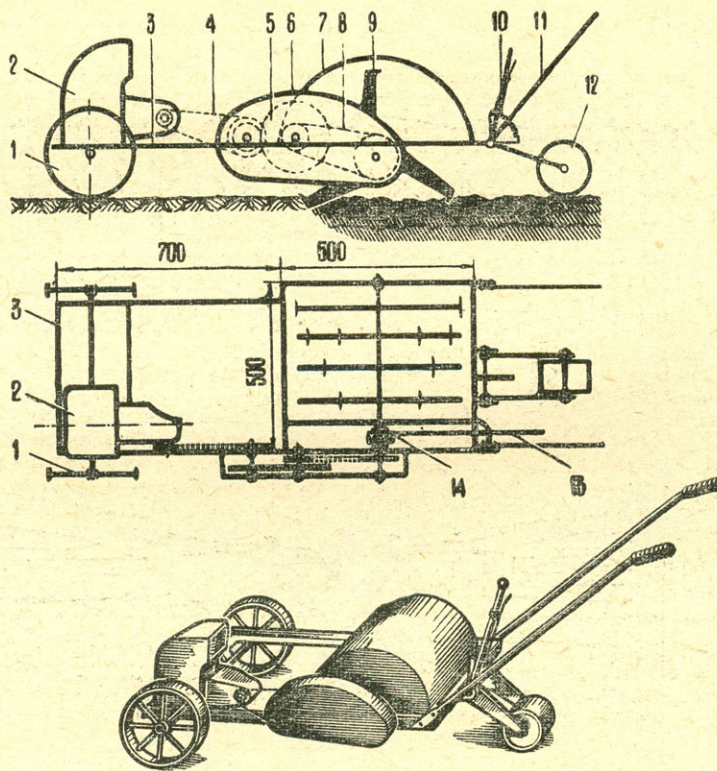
Общий вид и кинематическая схема почвообрабатывающей фрезы:
